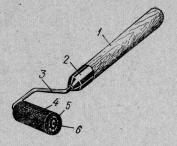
1 — ручка; 2 — колпачок: 3 — кронштейн; 4 — валик; 5 — корпус; 6 — ось
